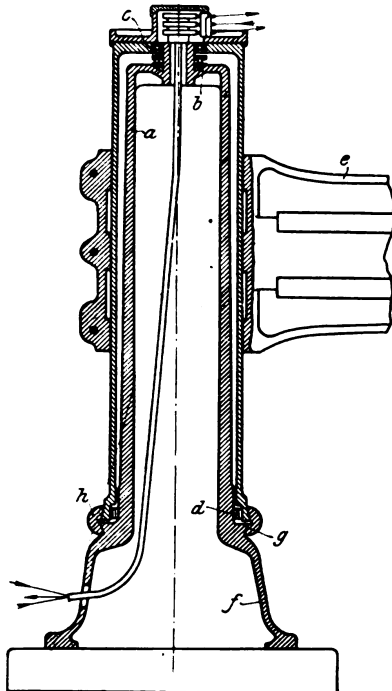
Schnitt durch die Säule der Raboma- Radialbohrmaschinen.
